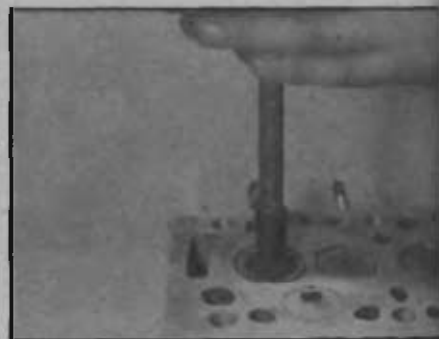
Притирка рабочей поверхности тарелки клапана
